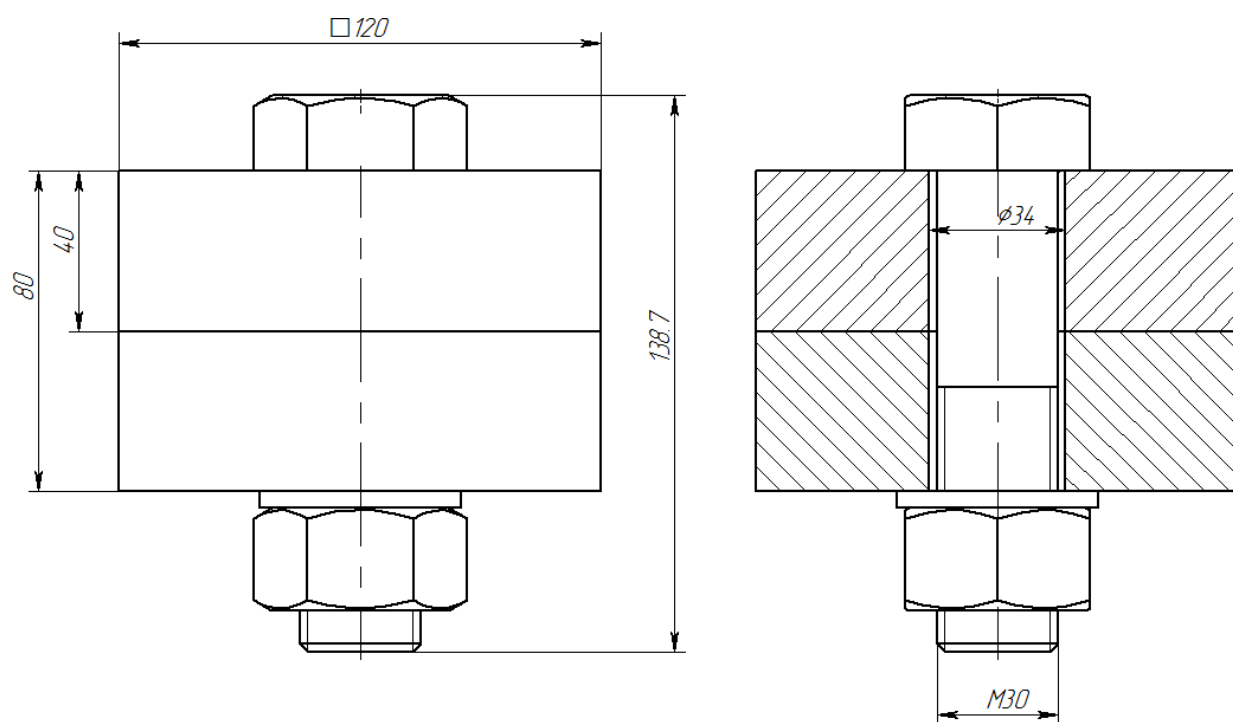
Готовый 2D чертёж болтового соединения
